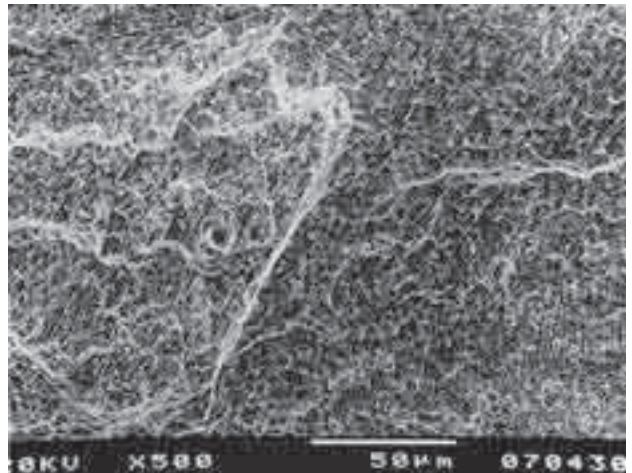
MEV da fratura dúctil por rasgamento do corpo-de-prova na condição soldado a laser; 500 X.
